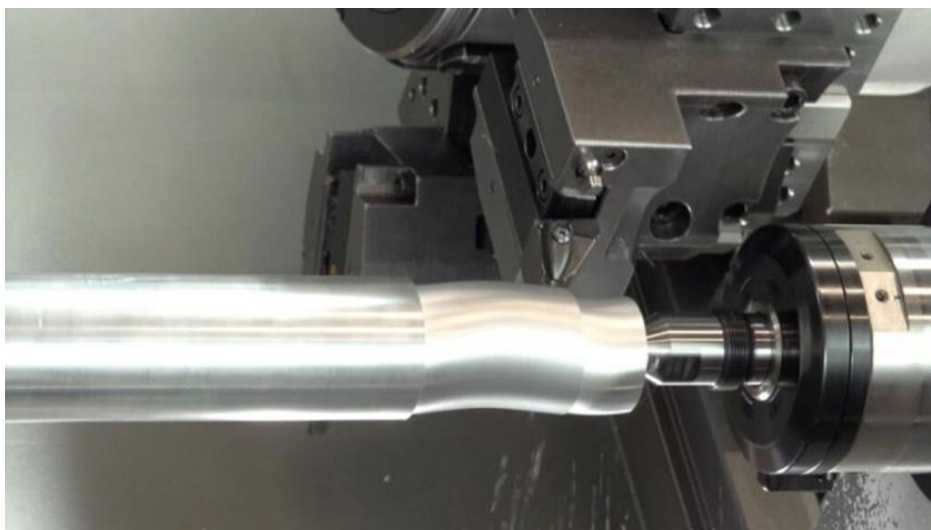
Процес токарного оброблення ексцентрикових поверхонь
